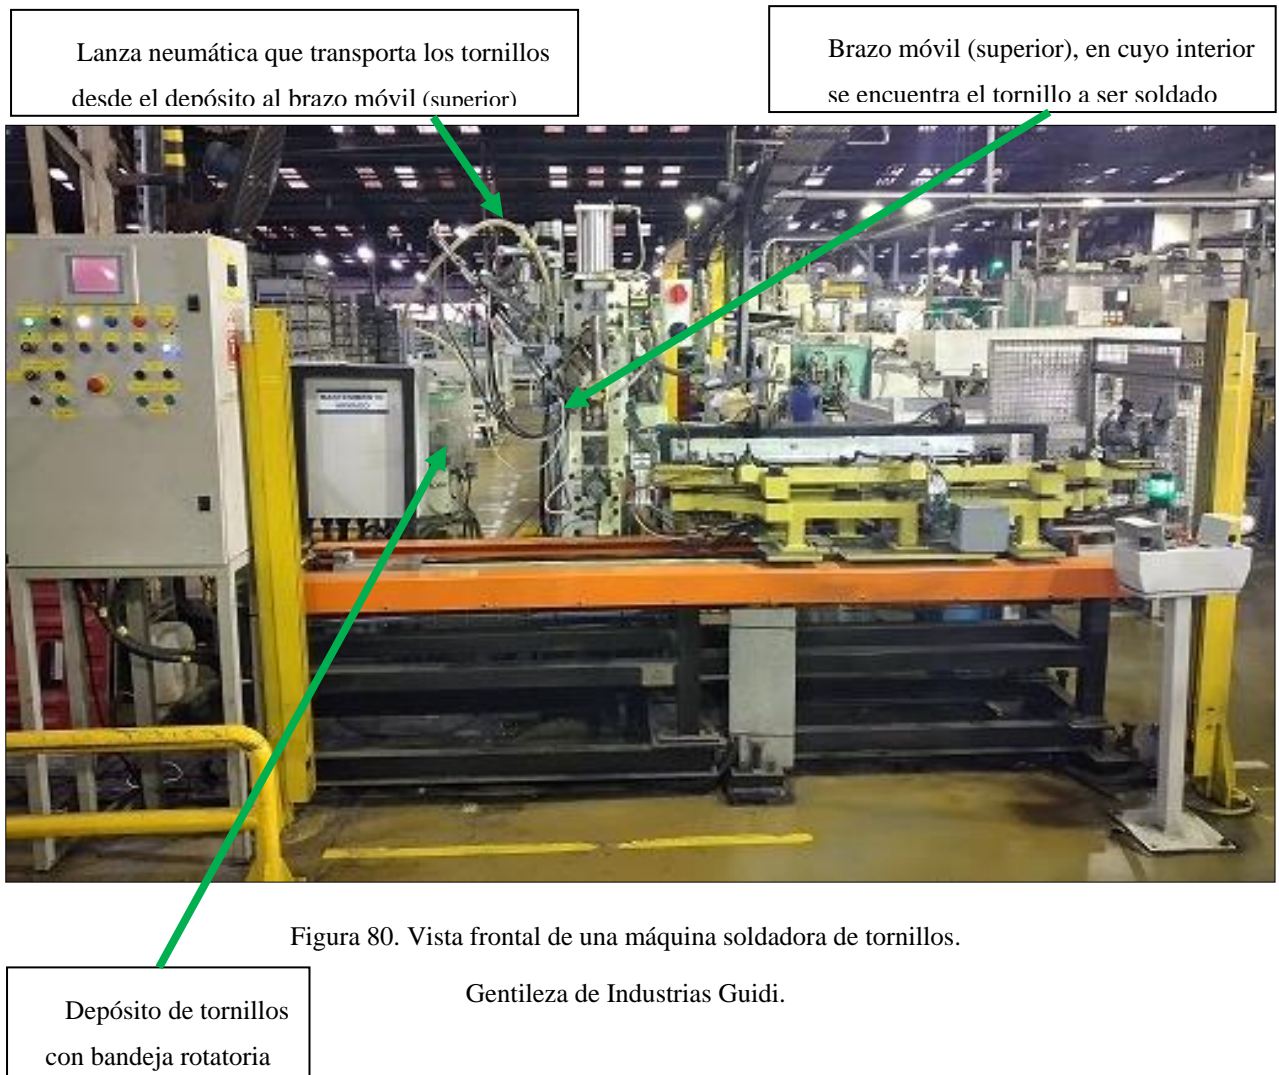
Vista frontal de una máquina soldadora de tornillos.
